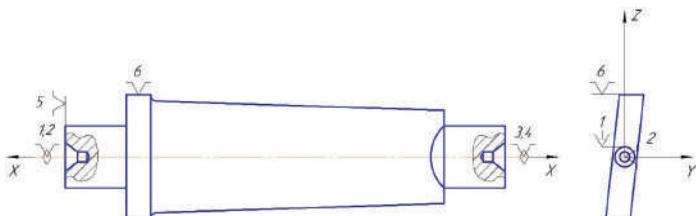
Схема базирования рабочей лопатки компрессора с хвостовиком типа ласточкин хвост с двумя центровыми отверстиями в технологических бобышках
